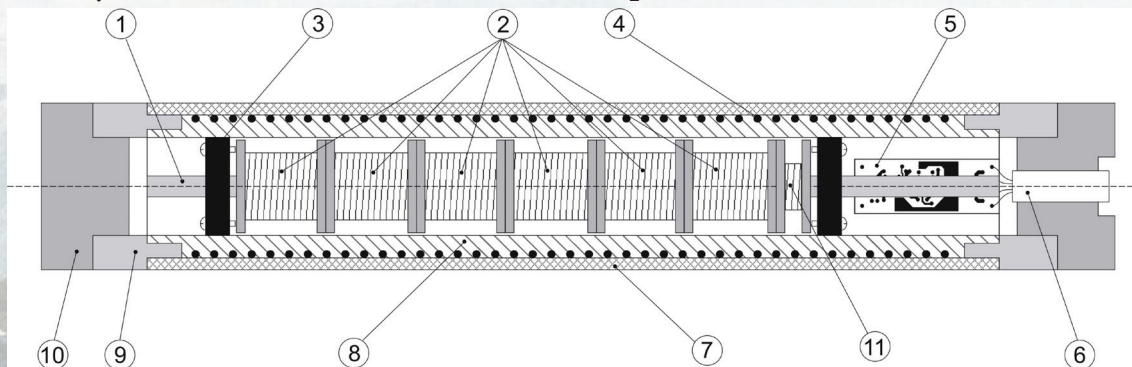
Конструкция индукционного датчика: 1 – ферромагнитный сердечник, 2 – секции измерительной катушки, 3 – резиновый уплотнитель, 4 – градуировочная катушка, 5 – предварительный усилитель, 6 – разъем, 7 – внешний корпус, 8 – внутренний корпус (экран), 9 – фиксирующий цилиндр, 10 – заглушка, 11 – дополнительная безиндуктивная катушка.
